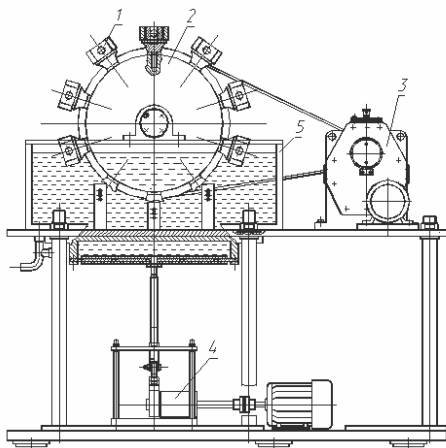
Обладнання для промивання від стружки порожнин корпусу газового лічильника: 1 – деталь; 2 – диск; 3 – привод; 4 – вібропривод
